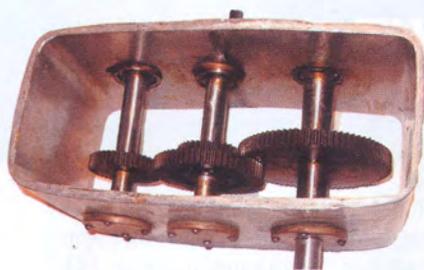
Редуктор с навитыми из ленты валами и корпусом
